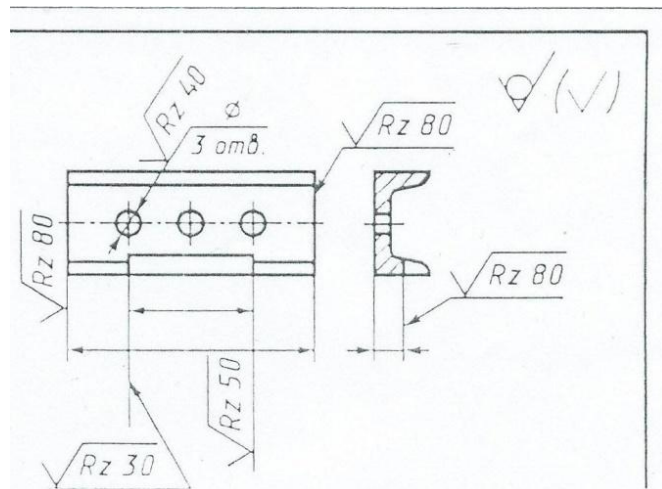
Обозначение шероховатости поверхности на чертежах деталей
